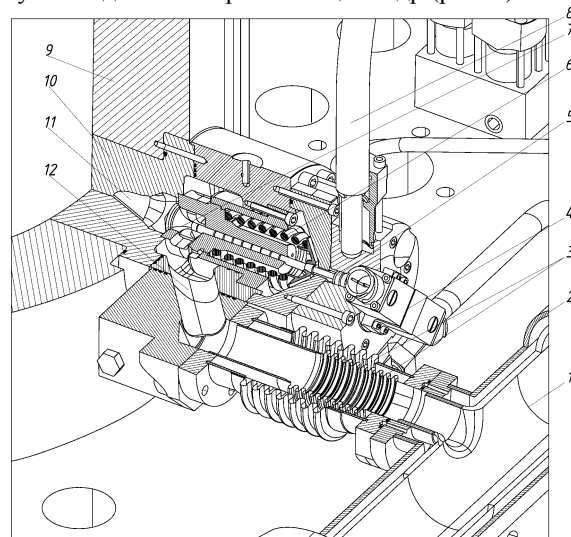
Установка газового клапана на втулке цилиндра двигателя RT-flex50DF: 1 – газовая магистраль; 2 – внешняя оболочка; 3 – внешний и внутренний сильфон; 4 – электромагнитный клапан управления; 5 – гидравлический поршень привода клапана; 6 – пружина закрытия клапана; 7 – газовый клапан; 8 – гидравлическая магистраль привода клапана; 9 – втулка цилиндра; 10 – корпус газового клапана; 11 – канал подвода ГТ в рабочий цилиндр; 12 – канал подвода ГТ к газовому клапану
